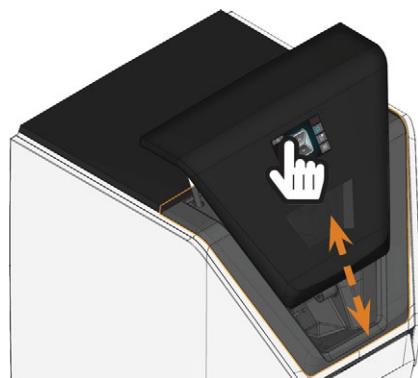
OUVRIR ET FERMER LA PORTE DE LA CHAMBRE DE TRAVAIL
